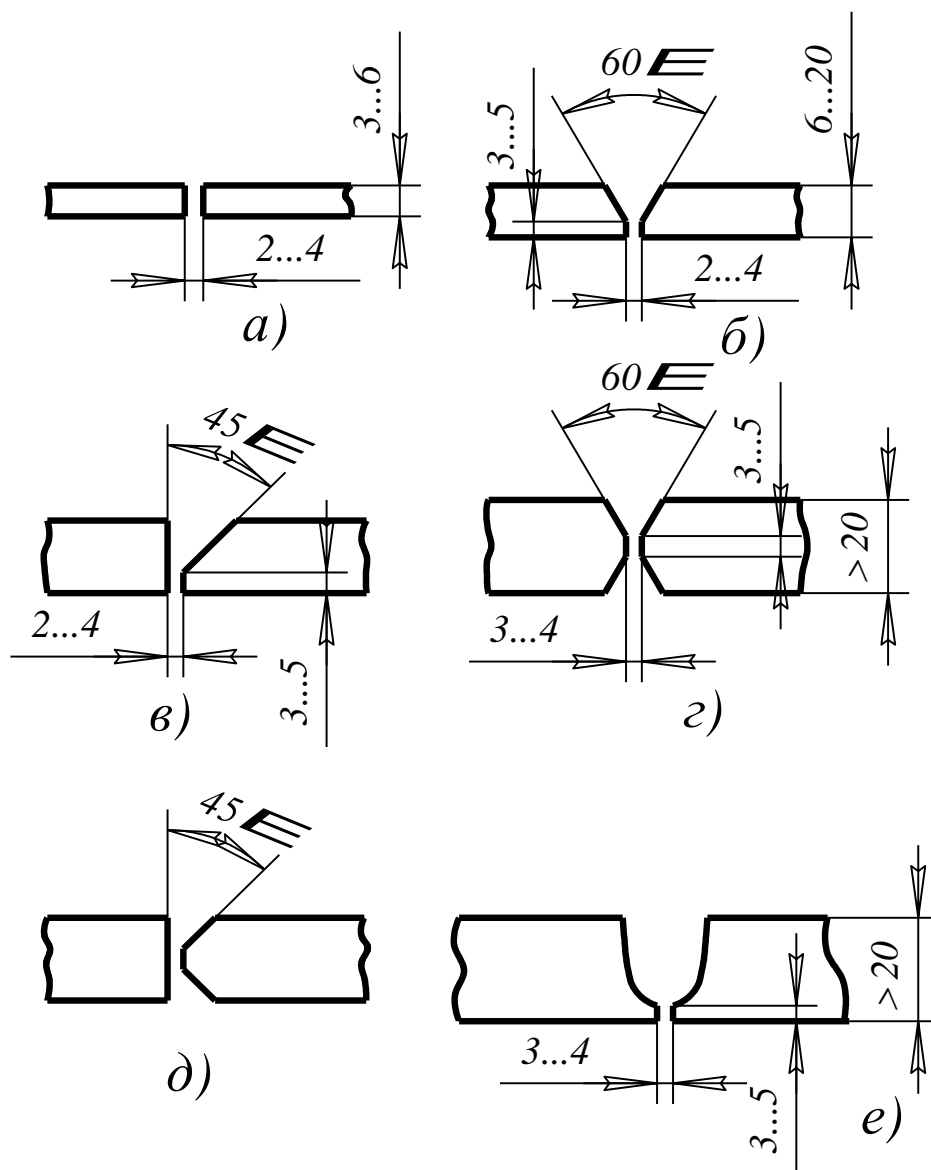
Підготовка кромки для ручного дугового зварювання встик
